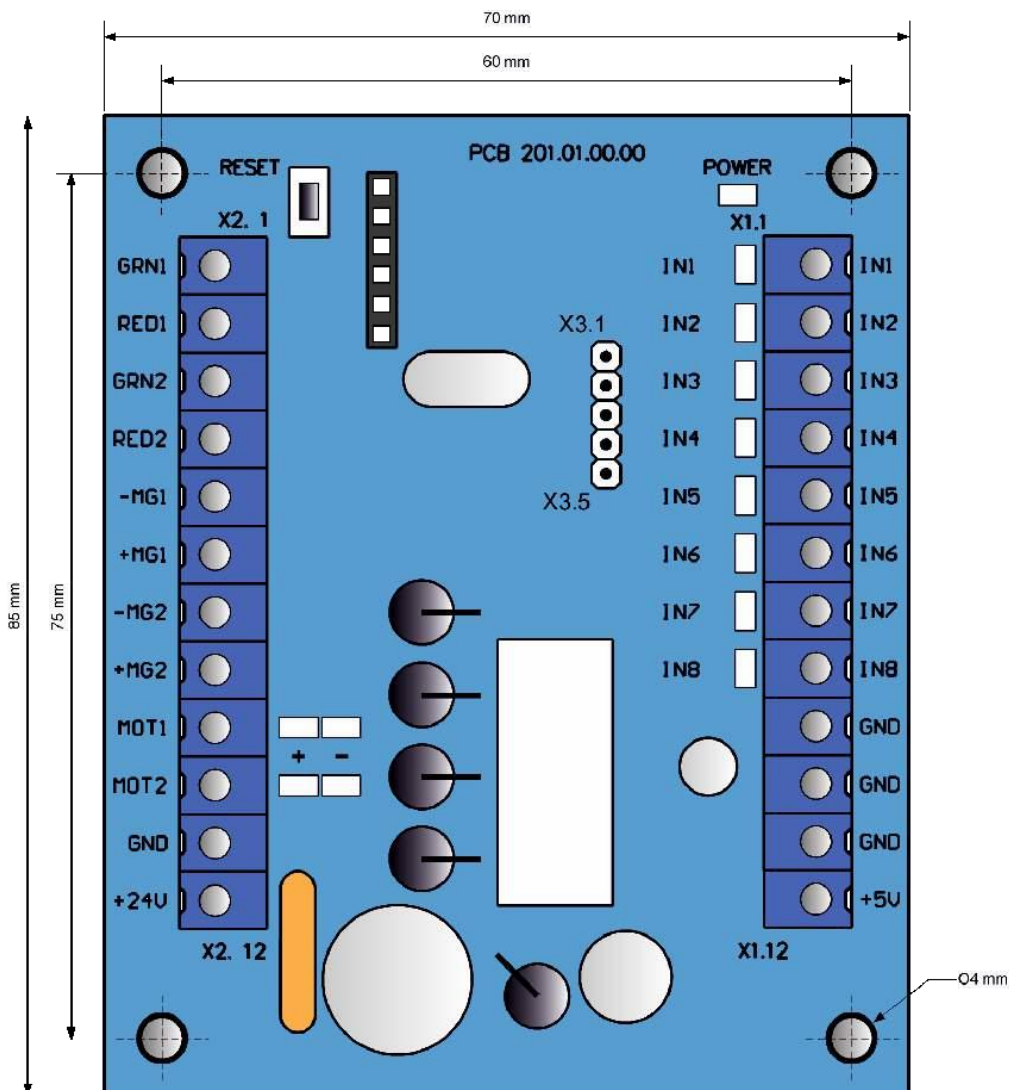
Внешний вид контроллера моторизированного механизма PCB.201.01.00.00
